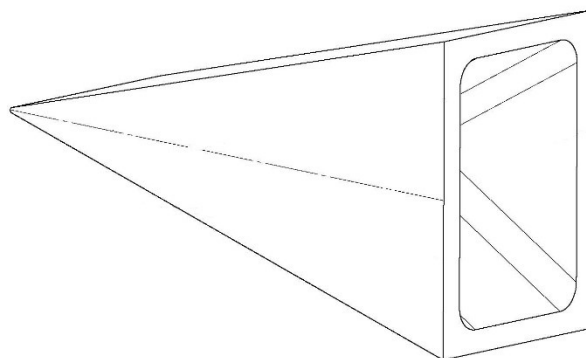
Схематическое изображение поковки коронки зуба ковша экскаватора
